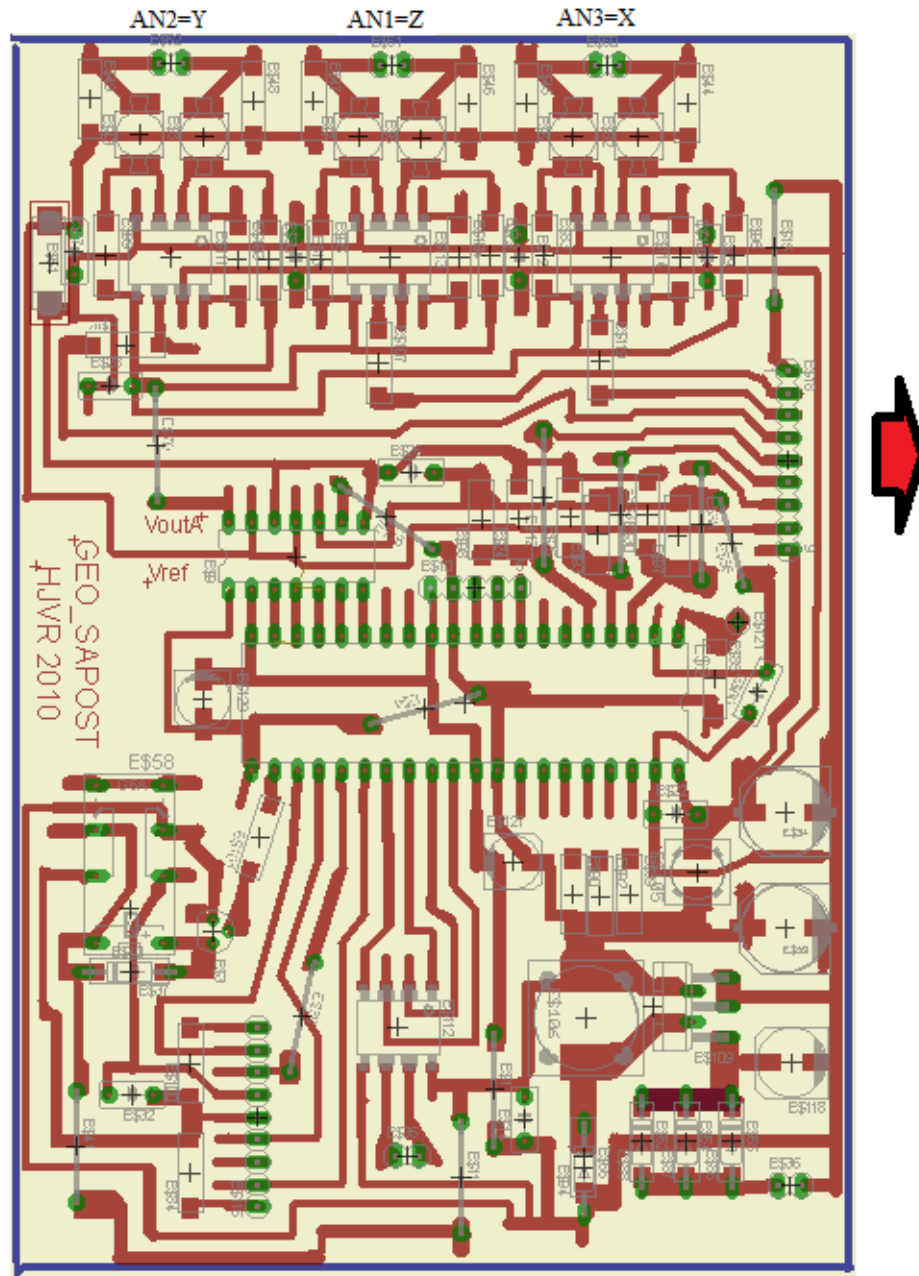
Placa PCB del geófono SAPOST (parte a).
